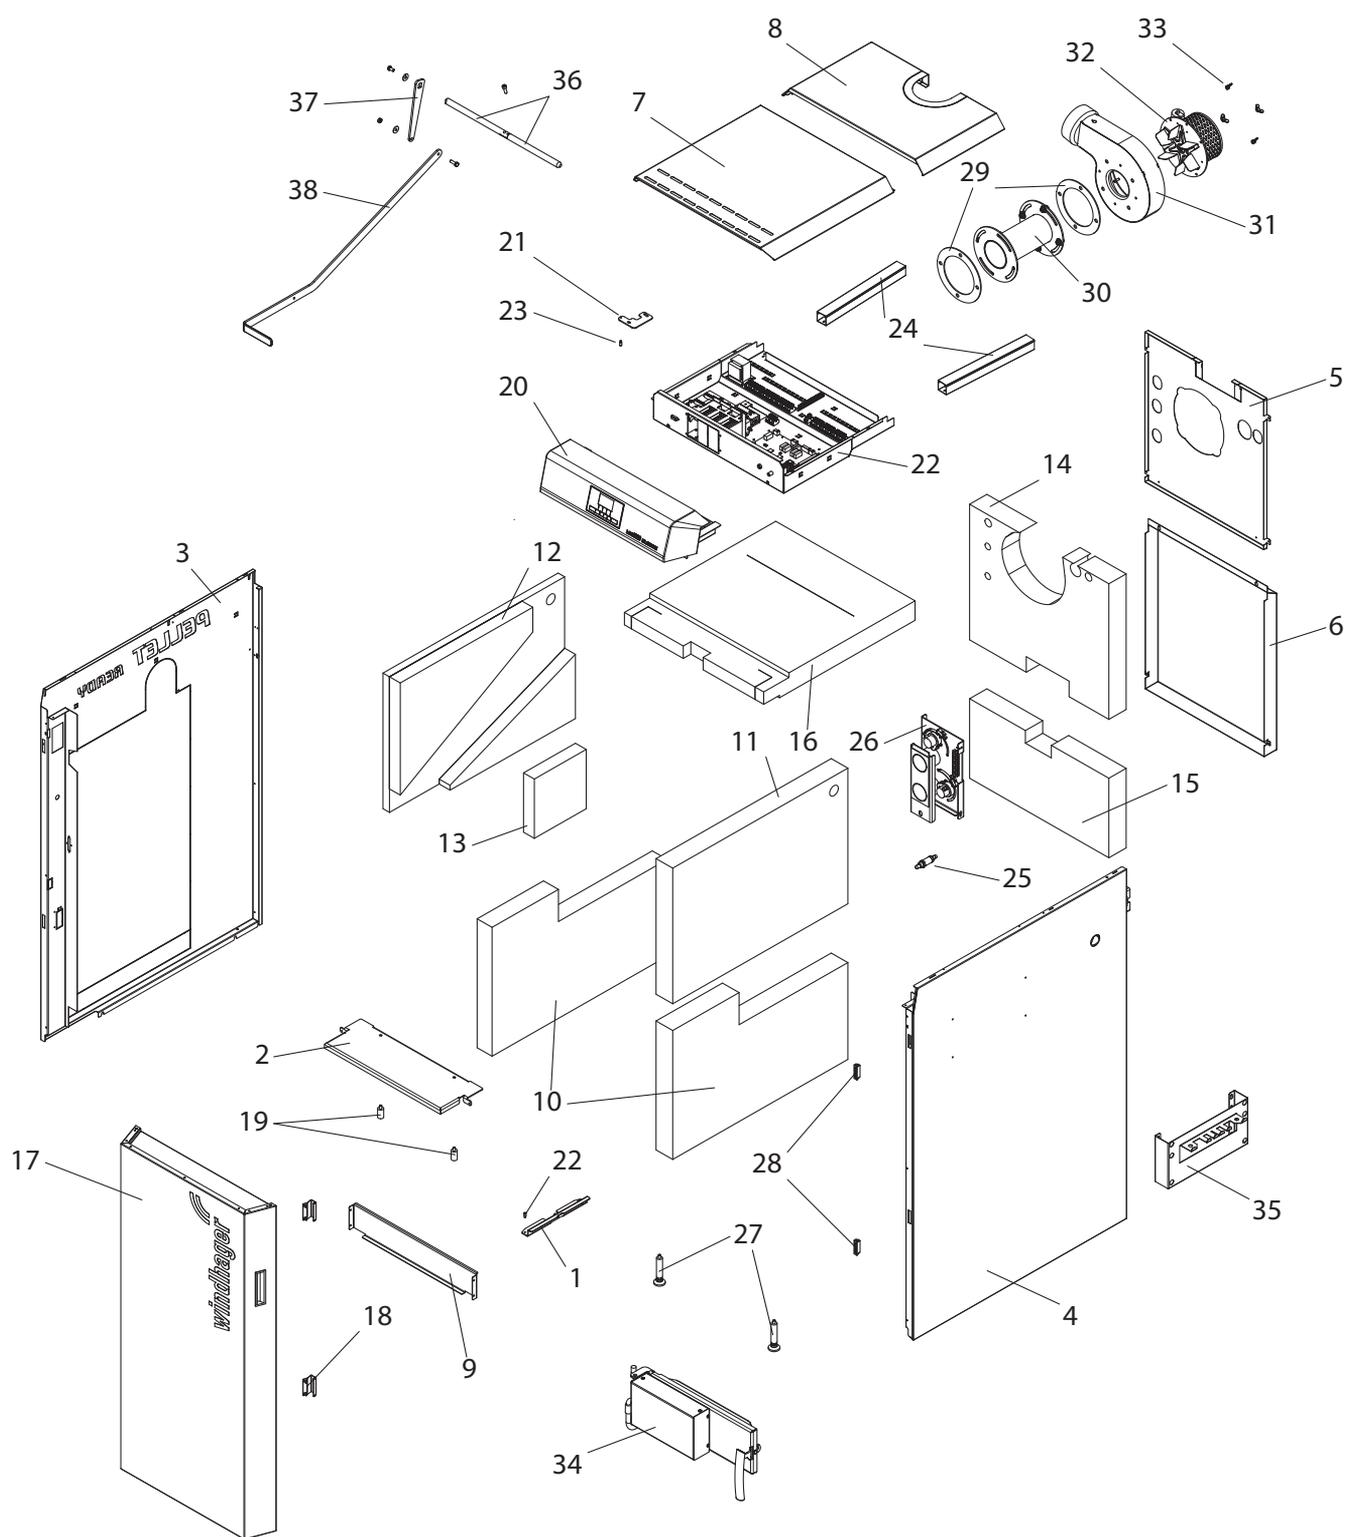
Parti per il montaggio della caldaia a gassificazione di legna
